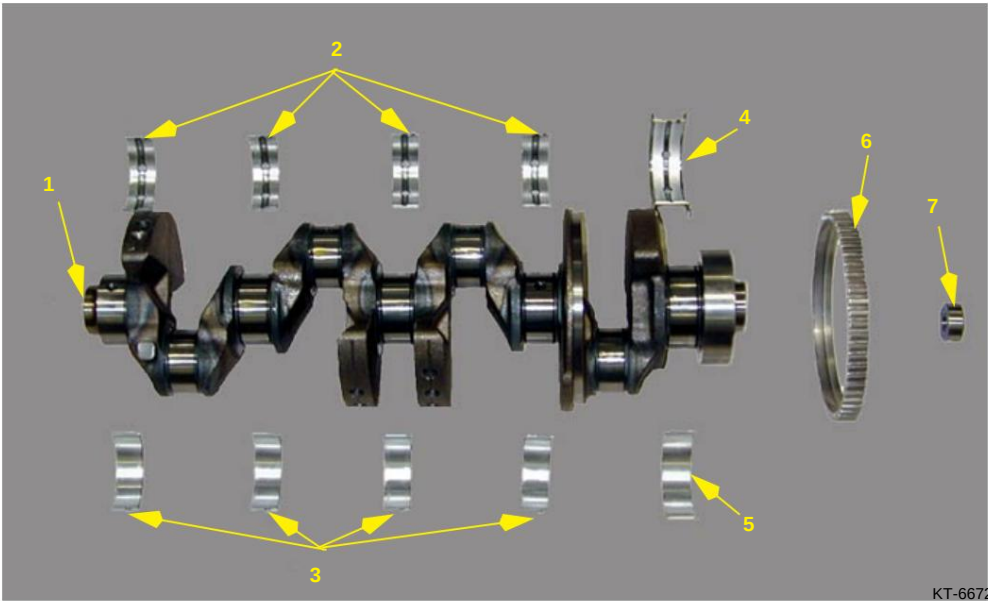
Virabrequim com rolamentos e roda dentada incremental
